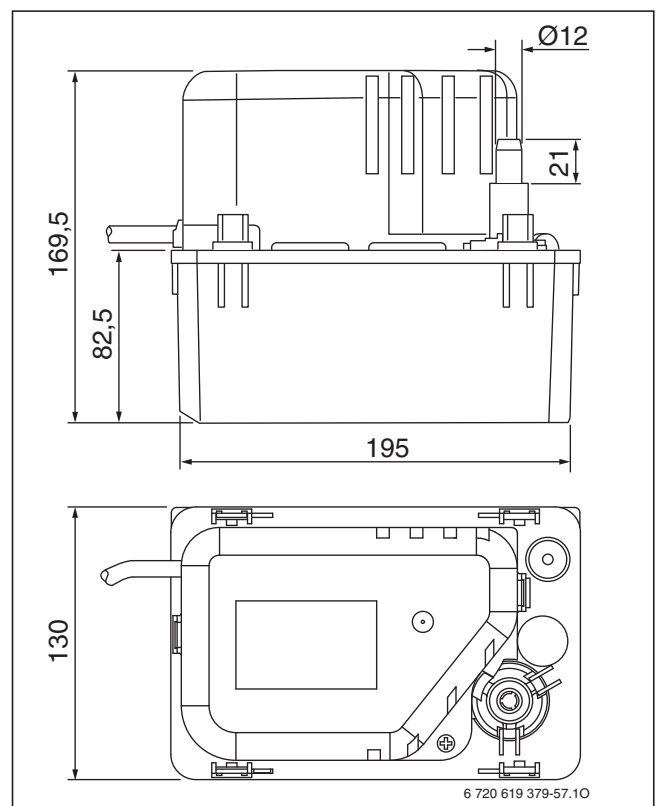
Abmessungen Wilo-DrainLift Con (Maße in mm)
